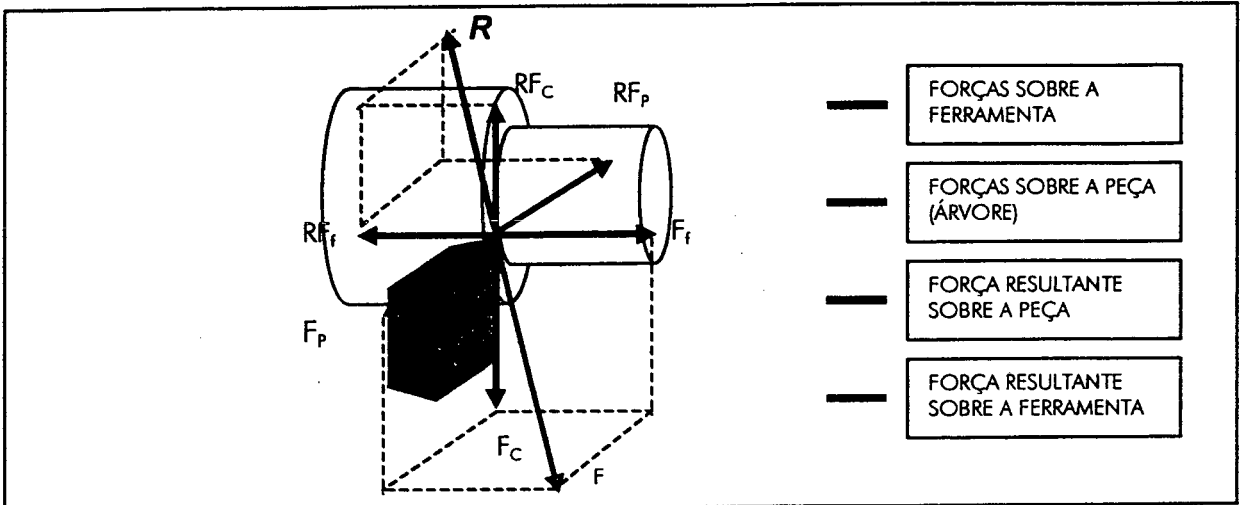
Componentes da força de usinagem no torneamento – DIN 6584 [36].
